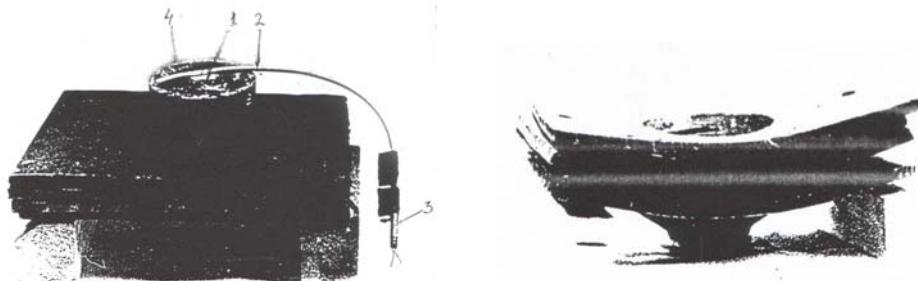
Вид сборки до и после испытаний: 1 - усилитель из пластита; 2 – ДШ; 3 – ЭД; 4 – заряд КВМ
